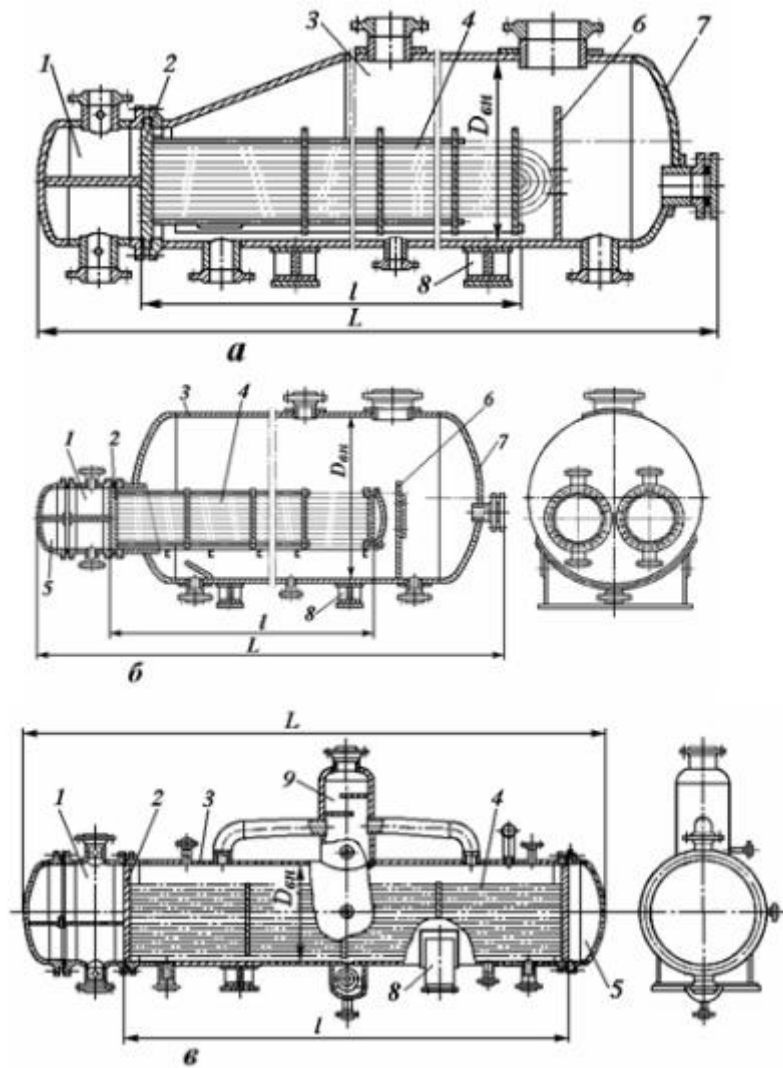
Теплообмінники - випарники з паровим простором: а - з конічним днищем і U- подібними трубками; б - з плаваючою головкою і двома трубними пучками; в - кожухотрубний з сухопарником; 1 - розподільна камера; 2 - трубна решітка; 3 - корпус; 4 - трубчатка; 5 - кришка еліптична; 6 - переливна планка; 7 - днище; 8 - опора; 9 - сухопарник.
